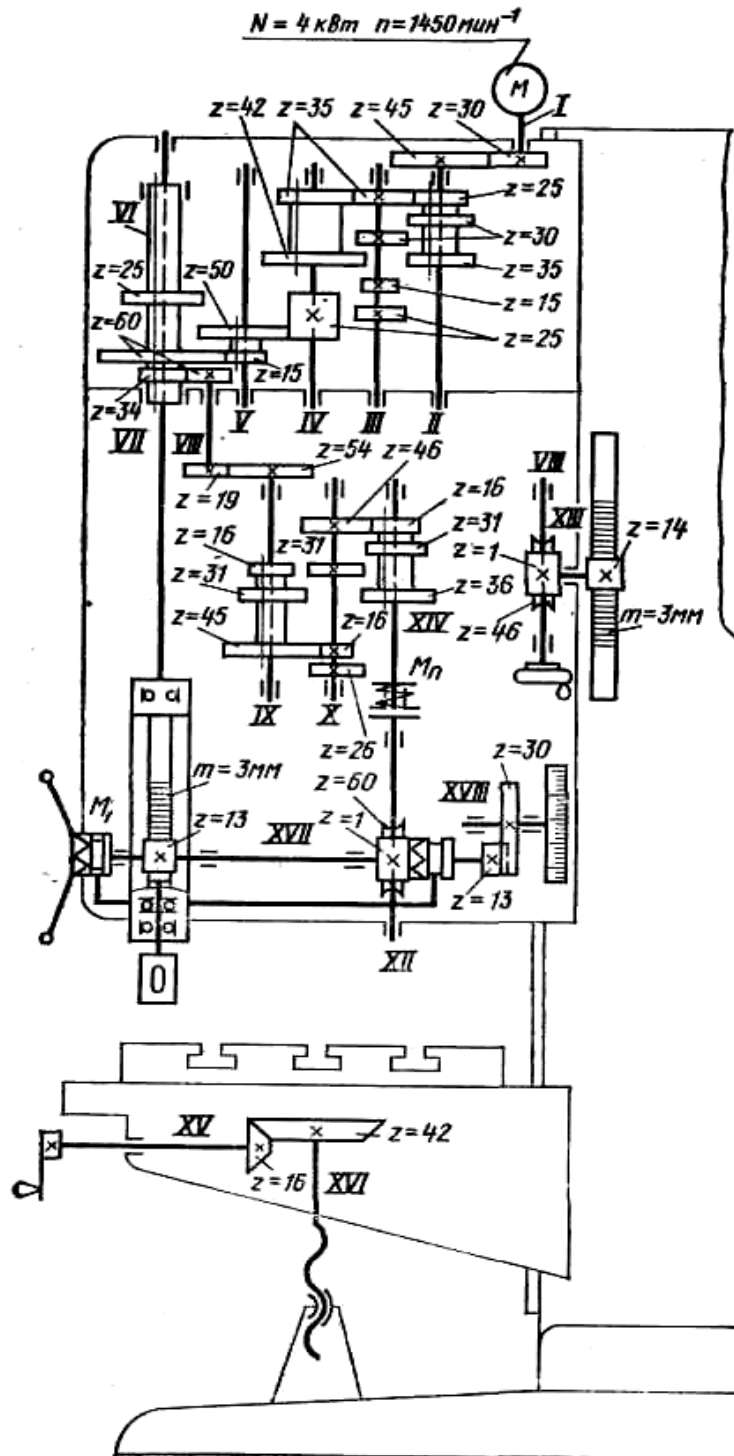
Кинематическая схема вертикально-сверлильного станка модели 2Н135
